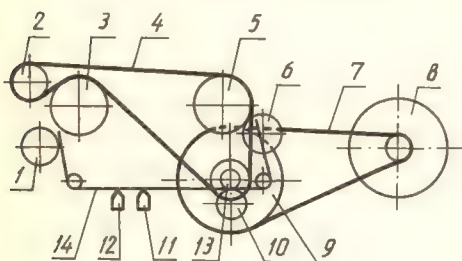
Кинематическая схема однодвигательного лентопротяжного механизма кассетного магнитофона с двумя пассивками
